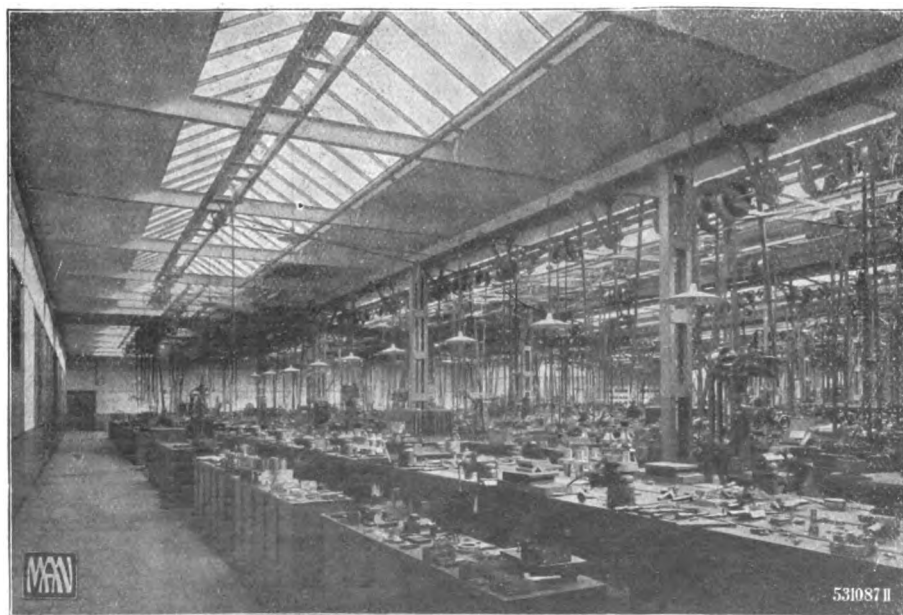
Werkzeugmaschinen-Werkstätte A. H. Schütte, Köln-Ehrenfeld
